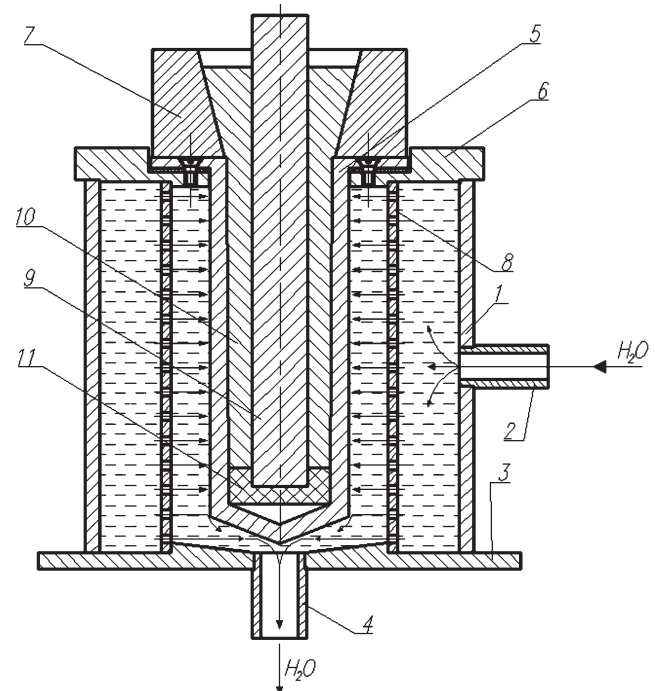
Схема литья биметаллической отливки в кристаллизатор со струйной системой охлаждения: 1 – корпус; 2 – подводящий патрубок; 3 – нижний фланец; 4 – отводящий патрубок; 5 – гильза; 6 – верхний фланец; 7 – захват; 8 – экран; 9 – стальной стержень; 10 – силумин; 11 – центровая шайба
